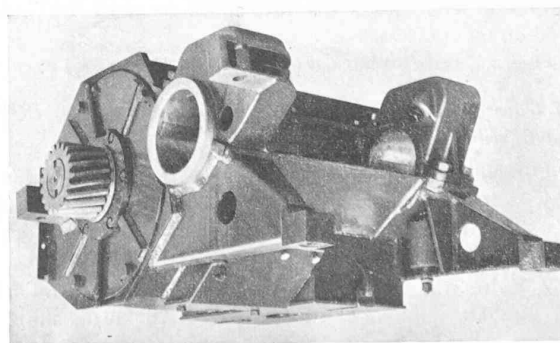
Moteur monophasé 240 PS, à carcasse entièrement soudée.
